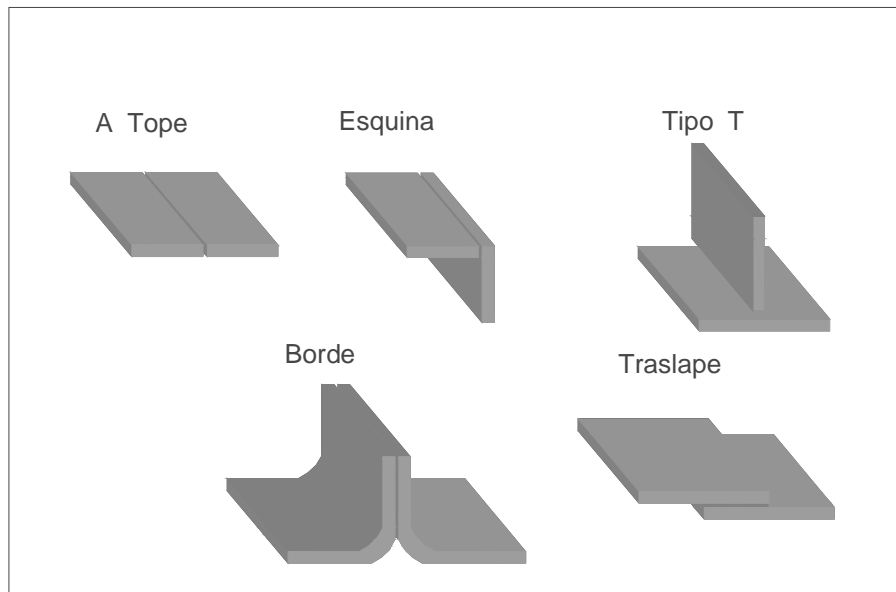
Estilos básicos de unión (Manual indura_ soldadura, Pág. 15).
